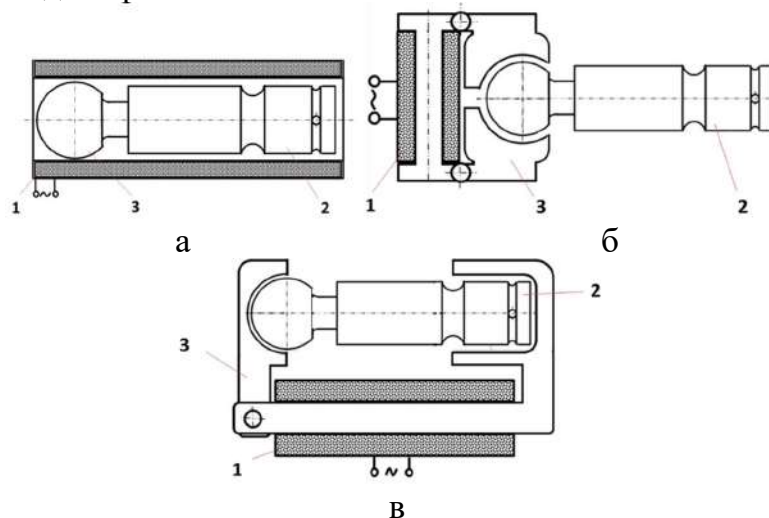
Різноманітні схеми магнітної обробки поршнів в зборі: а - схема обробки сфери шатуна; б - схема обробки сфери шатуна; в - схема обробки сфер шатуна і робочої частини поршня.
